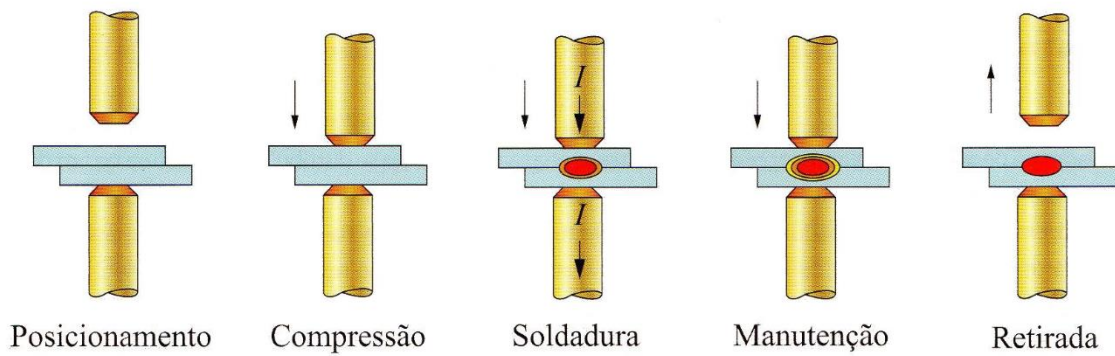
Diferentes etapas de realização de uma soldadura por pontos [35]
